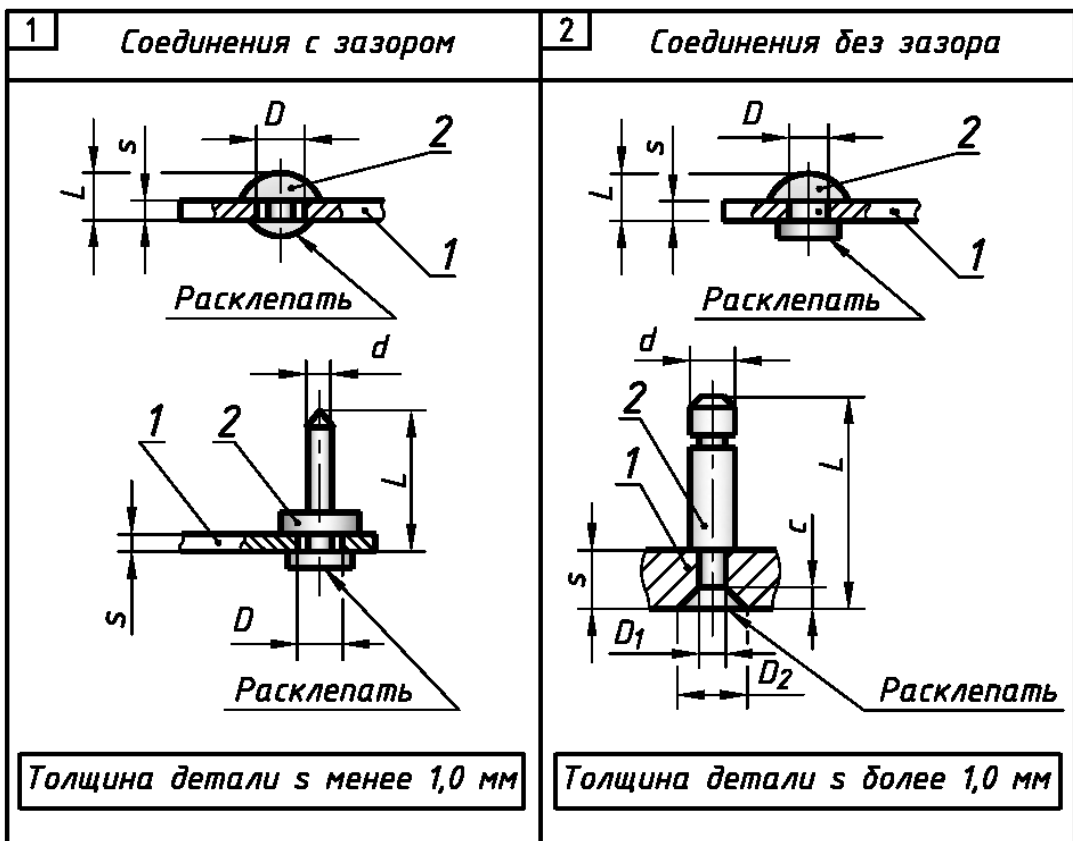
Варианты соединения деталей нестандартными заклепками и с цапфами
